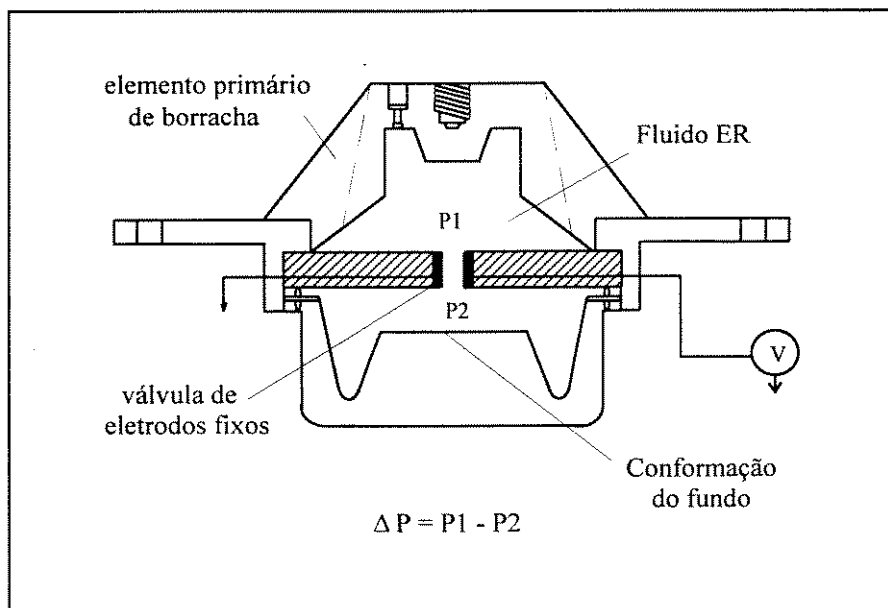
Suporte de máquinas que utiliza fluido ER – [duclo-88].
